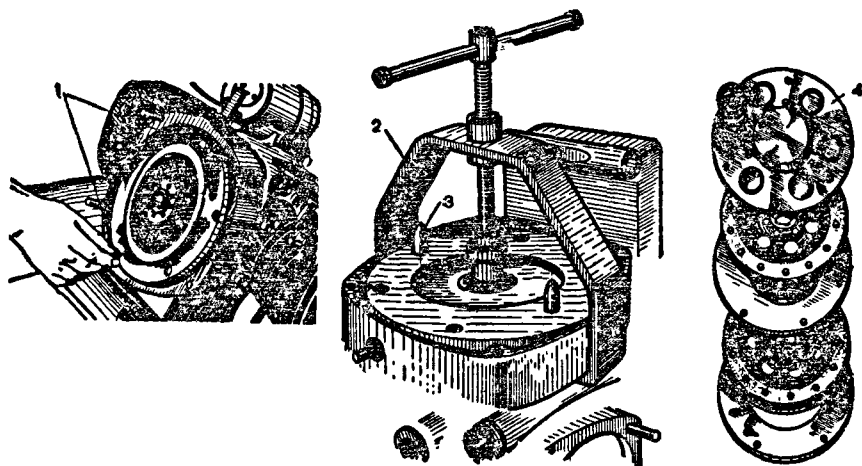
Сборка и разборка механизма сцепления; 1 — вспомогательные болты М8Х1; 2 — приспособление со шлицевым наконечником; 3 — направляющие болты; 4 — диски сцепления
